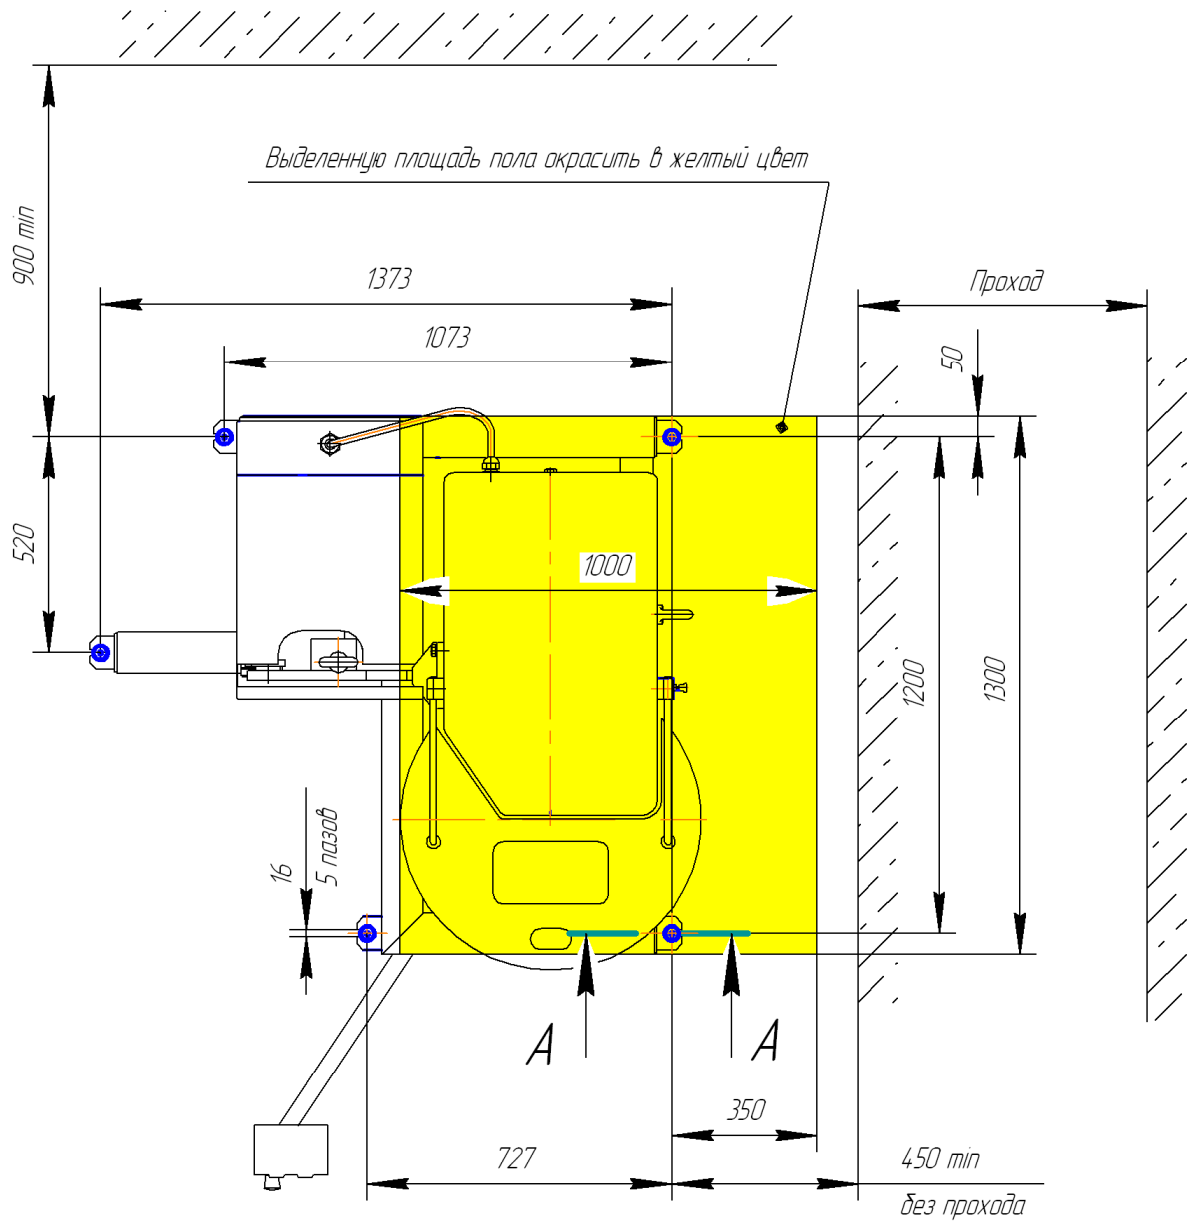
Схема размещения и установки фундаментных болтов.
